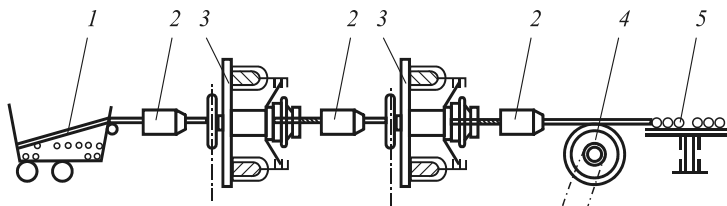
Схема агрегатов для сборки напорных рукавов бездорновым способом с разделением операций:
